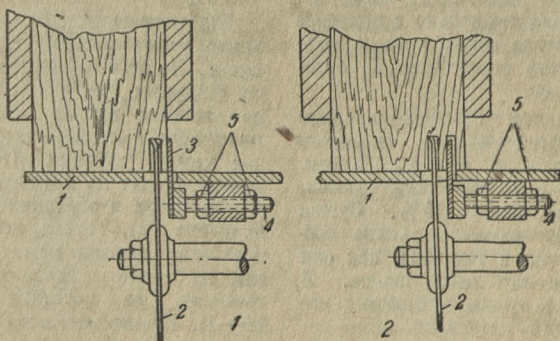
Фрезерование зубьев одной пилой с помощью делительной линейки
